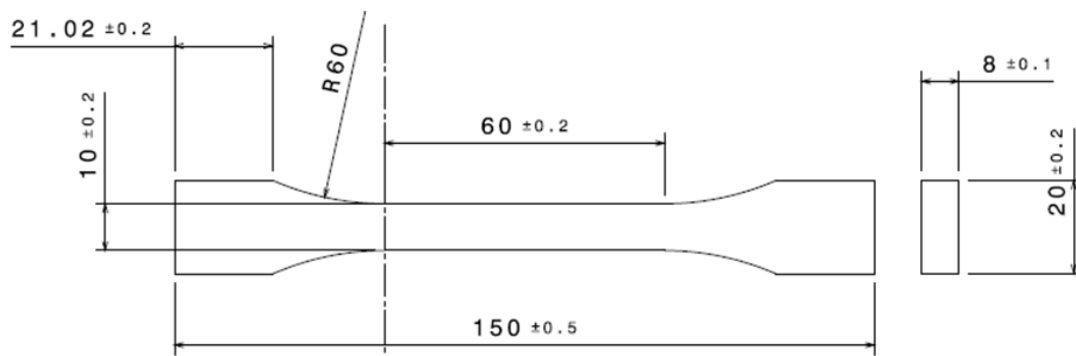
Géométrie et dimensions de l'éprouvette (mm)
